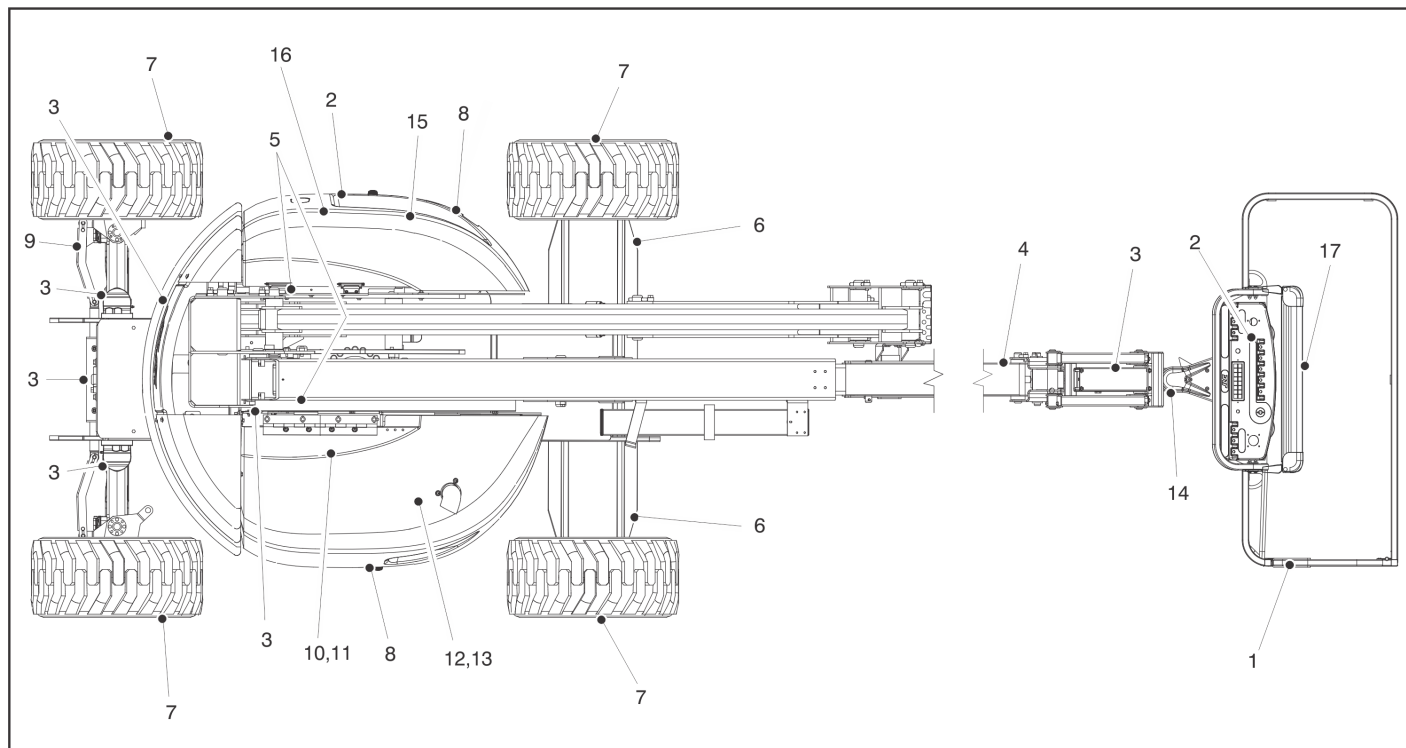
Daglig rundvandringsinspektion – blad 1 av 3
